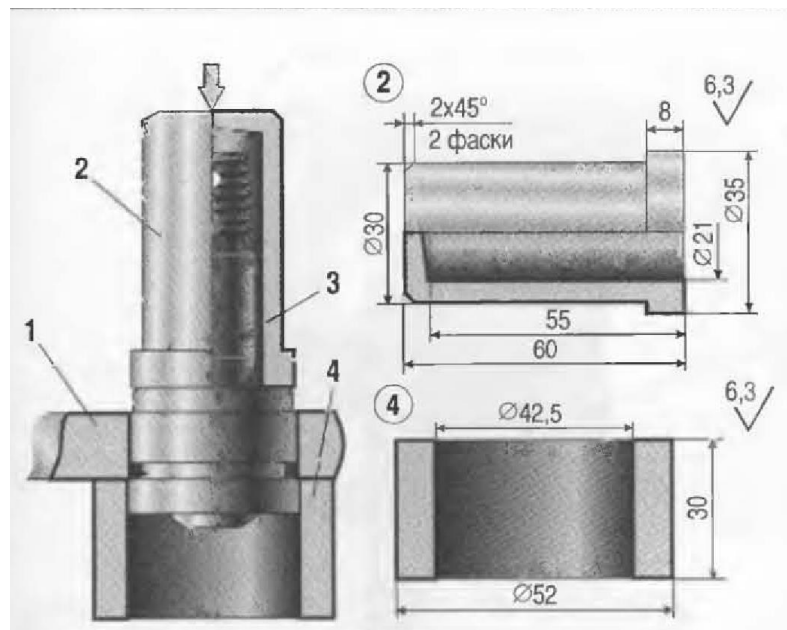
Вигляд випресовки для шарнірів рульової тяги:
